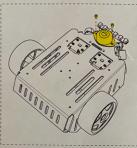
万向轮安装 Figure 7 Universal Wheel Installation
